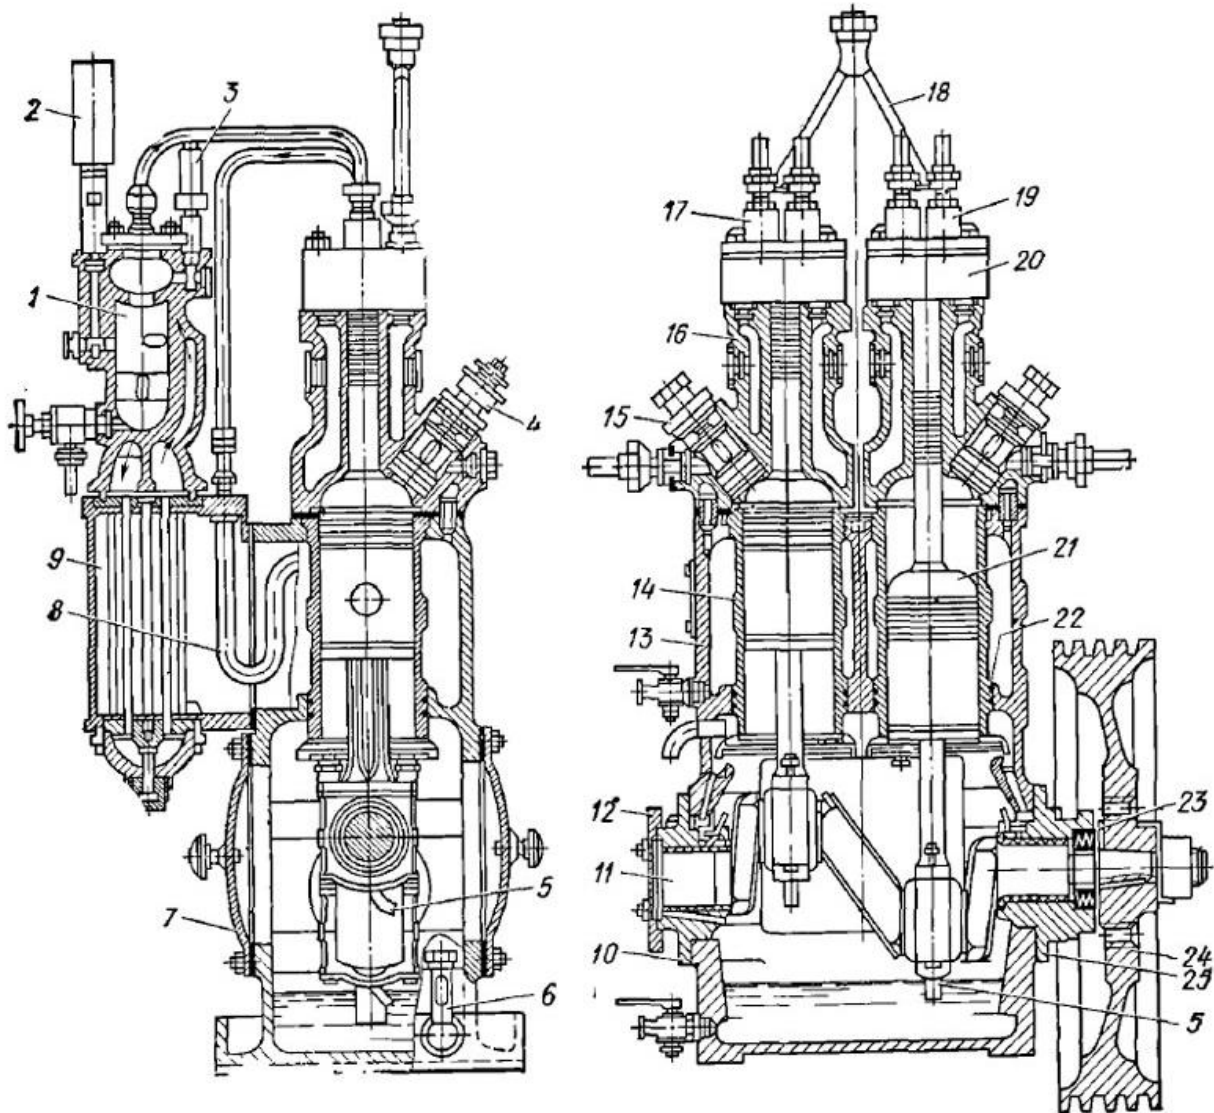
Конструкция двухступенчатого сдвоенного компрессора 20К-1
